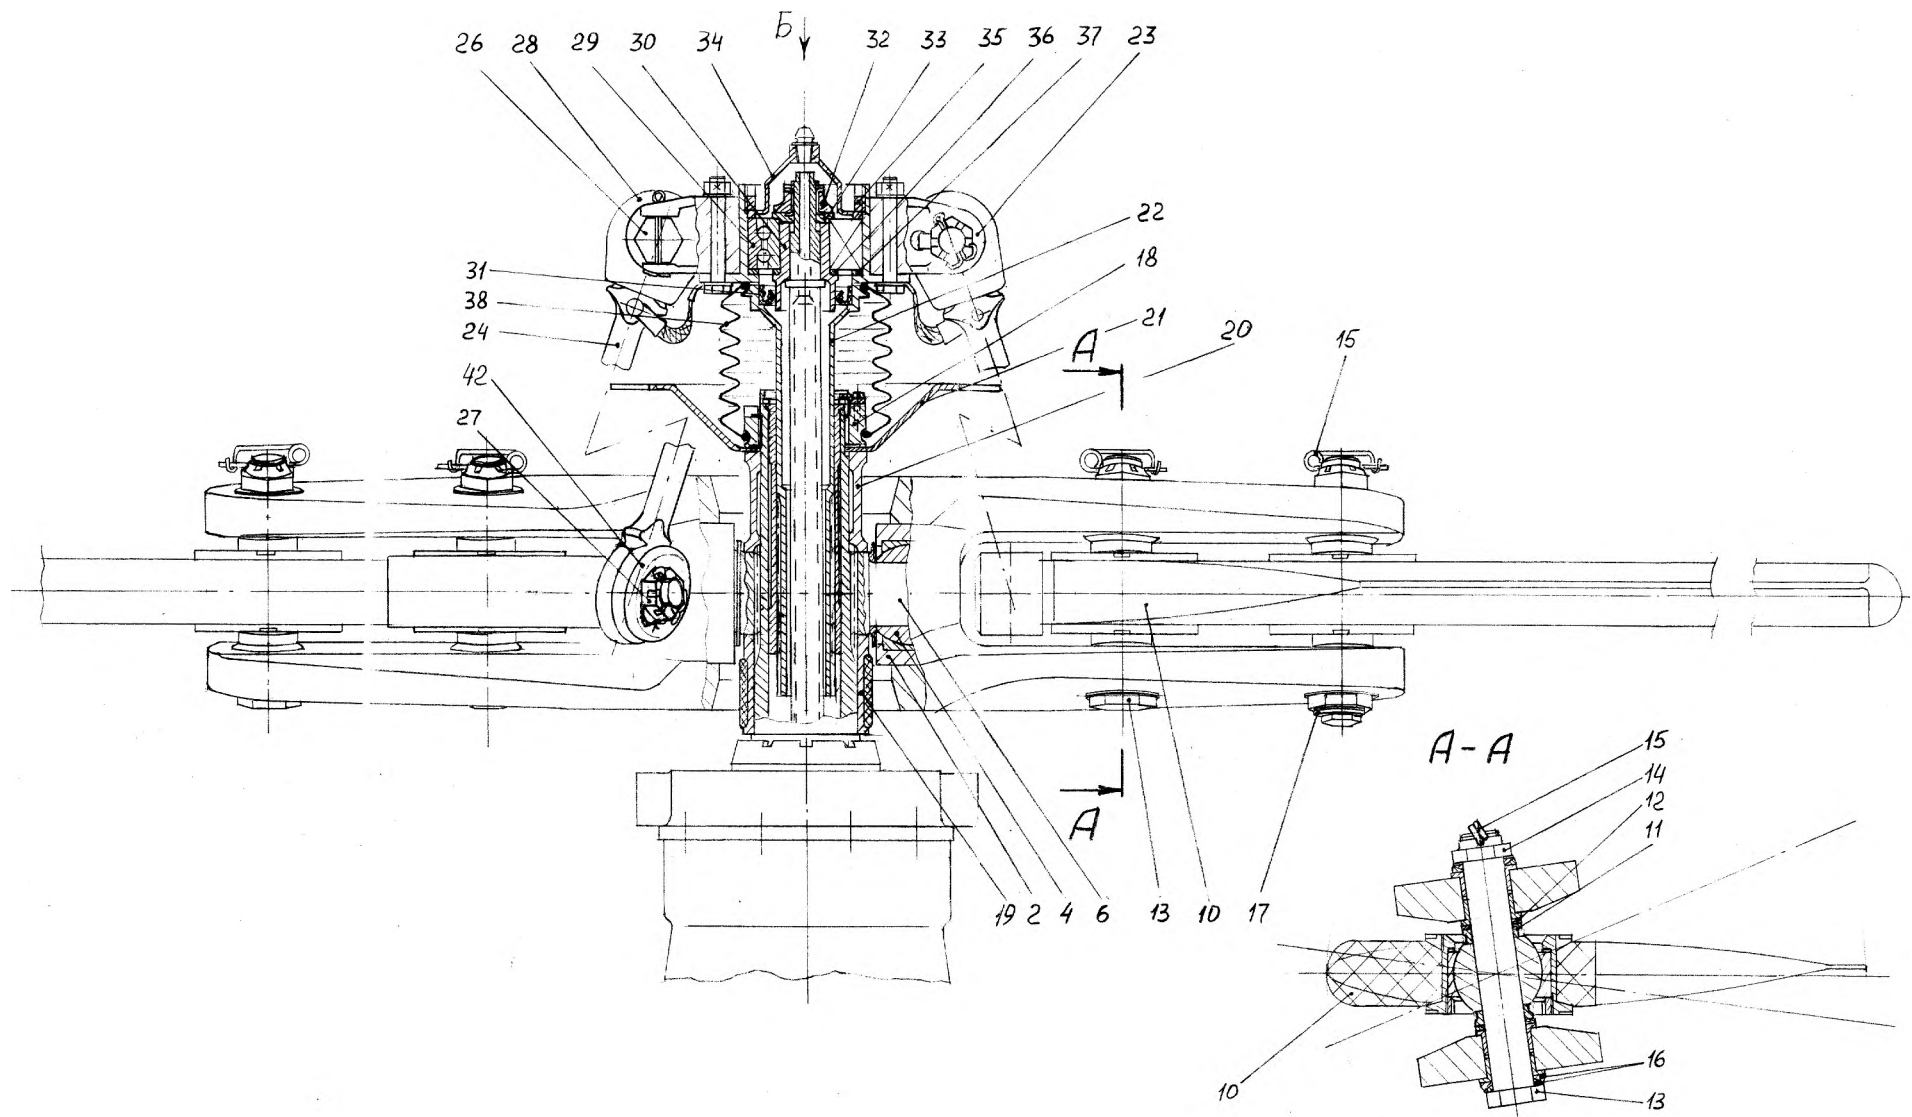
Конструкция втулки рулевого винта со сферическими подшипниками вертолета АНСАТ-У [16]:
